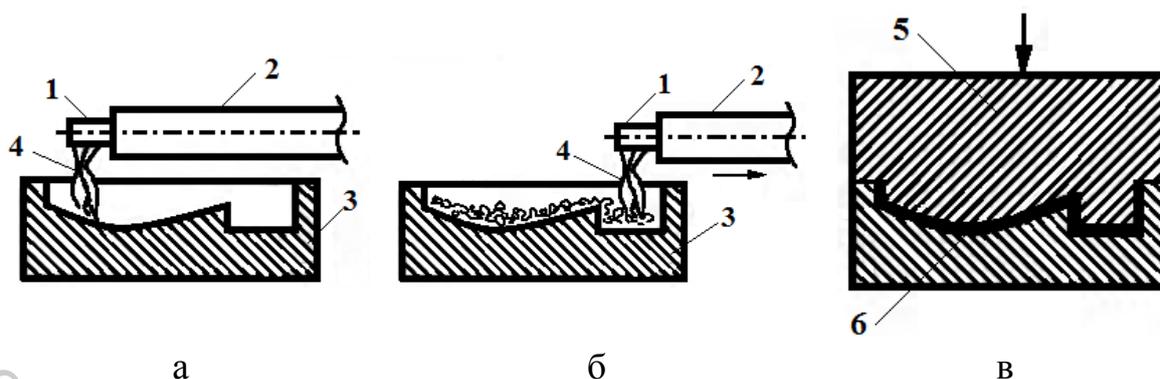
Стадии (а–в) инжекционно-прессового литейного способа формования резиновых смесей: 1 – сопло; 2 – нагревательный цилиндр; 3 – литейная форма; 4 – жгуты резиновой смеси; 5 – формующий пуансон; 6 – подошва
